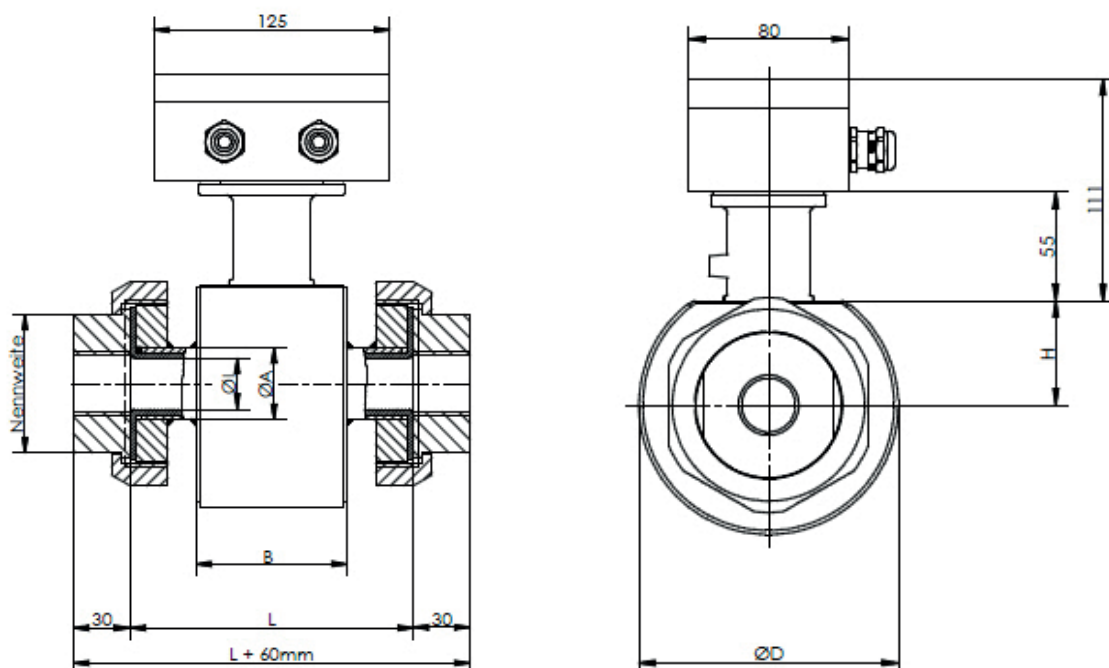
Bemaßung mag-flux® T4 PTFE mit Gewindeanschluss getrennte Bauform
